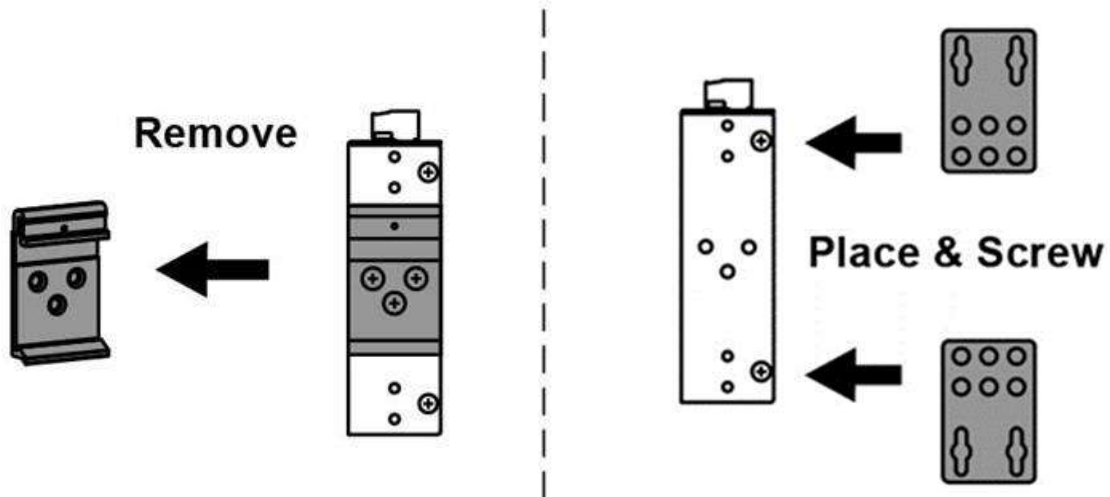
Retirez le support rail DIN du convertisseur et installez le support de montage mural
